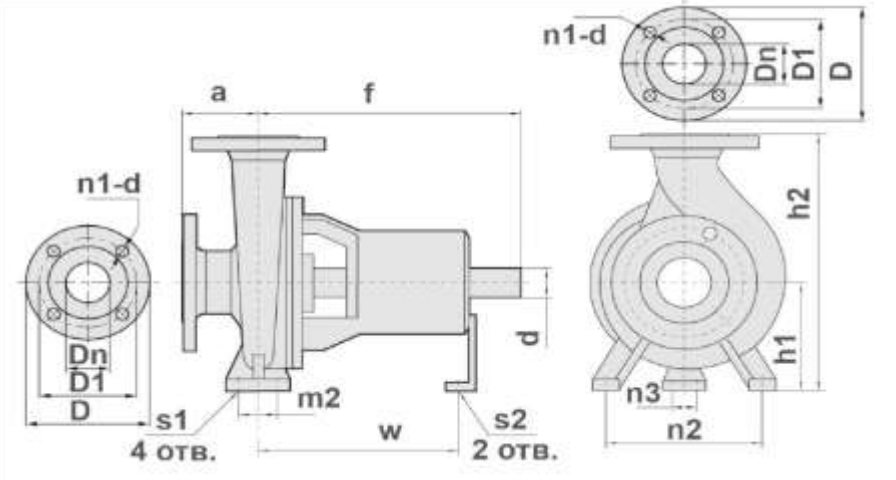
Насос с торцовым уплотнением со смазкой подшипников консистентной смазкой (изготавливается также со смазкой подшипников в масляной ванне, см. рис.1)
